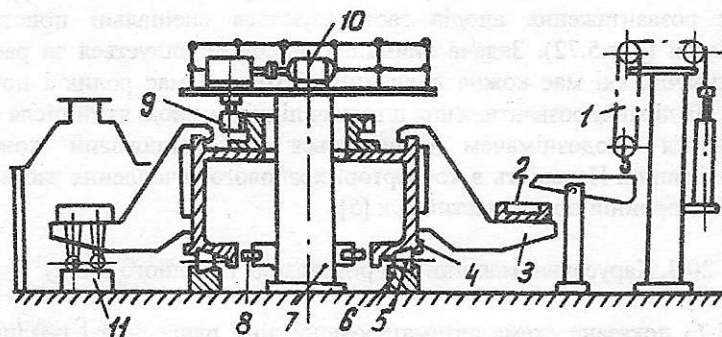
Схема карусельної машини для розливки свинцю: 1-заливний устрій; 2-виливниці; 3-кронштейни; 4-карусель; 5-опорні ролики; 6-кругові рейки; 7-колона; 8-центрувальні ролики; 9-приводна шестерня; 10-привод; 11-система зрошення
